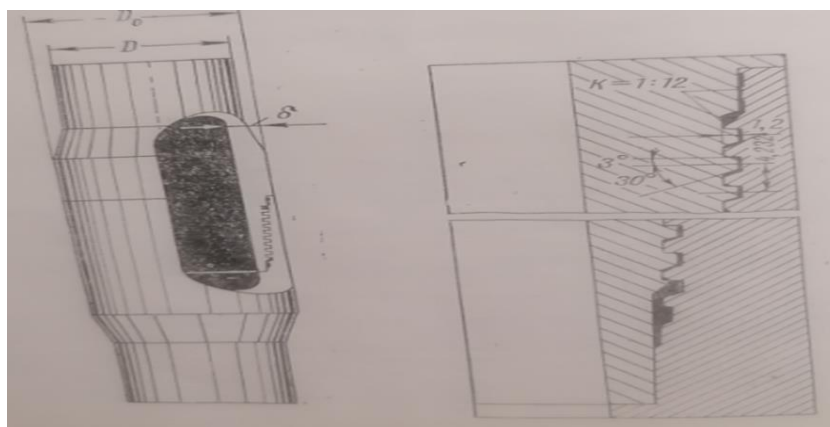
Насосно –компрессорные трубы НКБ-1
